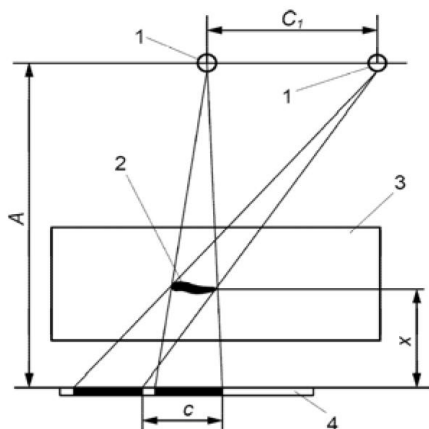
Схема визначення глибини розташування дефекту: 1 – випромінювач; 2 – дефект; 3 – дослідний зразок; 4 – реєструвальний пристрій
